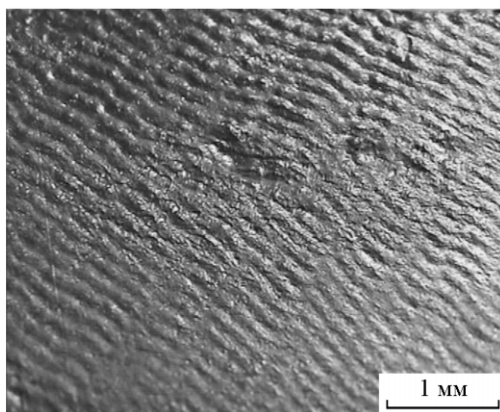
Внешний вид поверхности трехслойного медно-стального композита, полученного по батарейной схеме сварки взрывом ($\delta_2 = 2$ мм)
